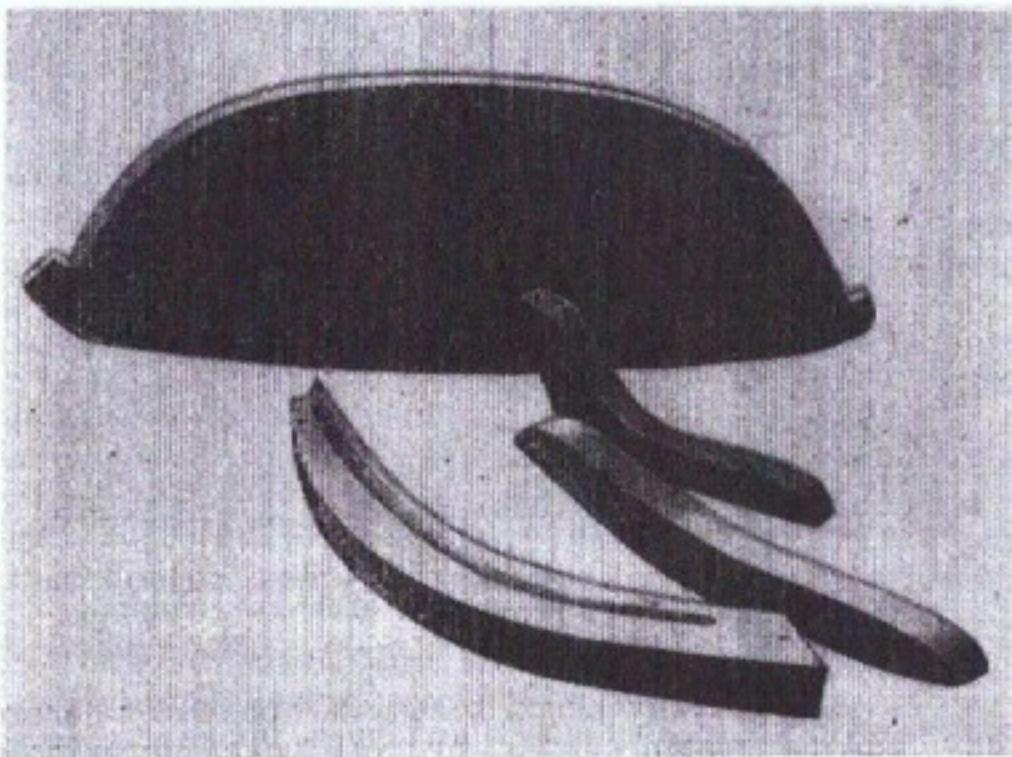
Образцы криволинейных деталей, обрабатываемых в цулагах.
